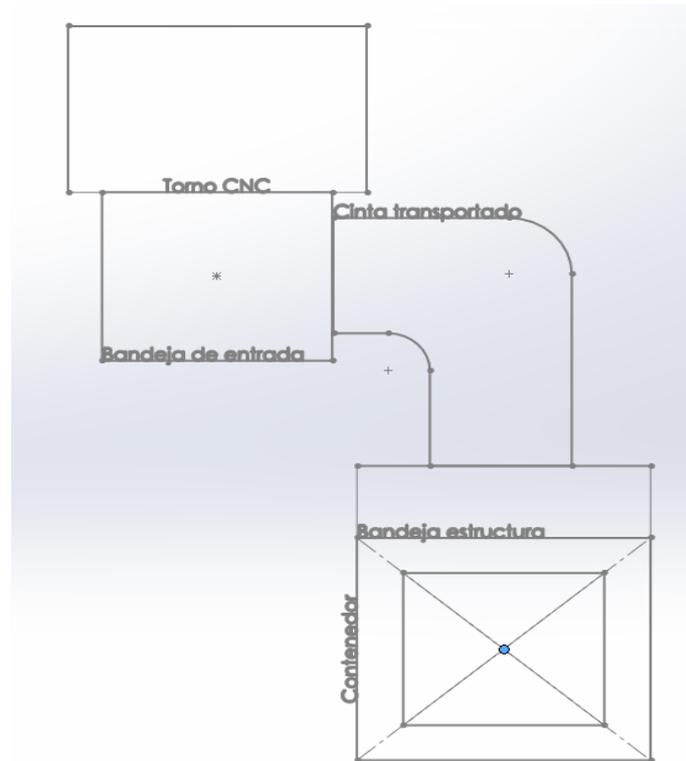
9: Vista en planta esquemática de sistema con banda horizontal
